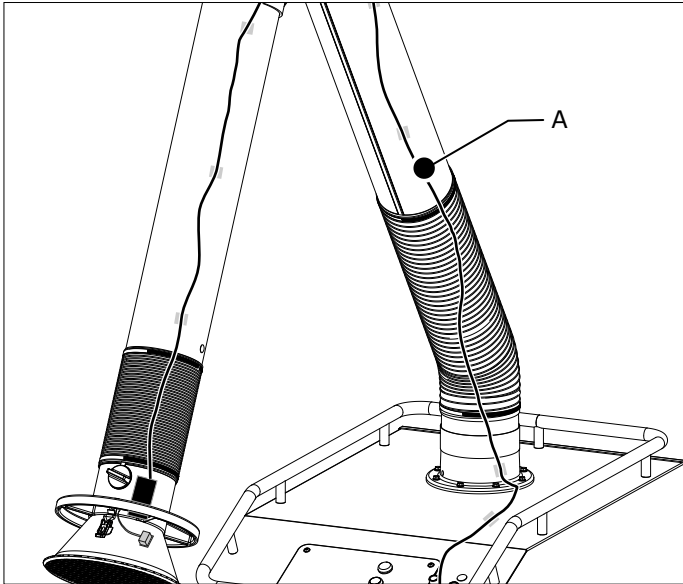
Montaggio del cavo della lampada di lavoro
